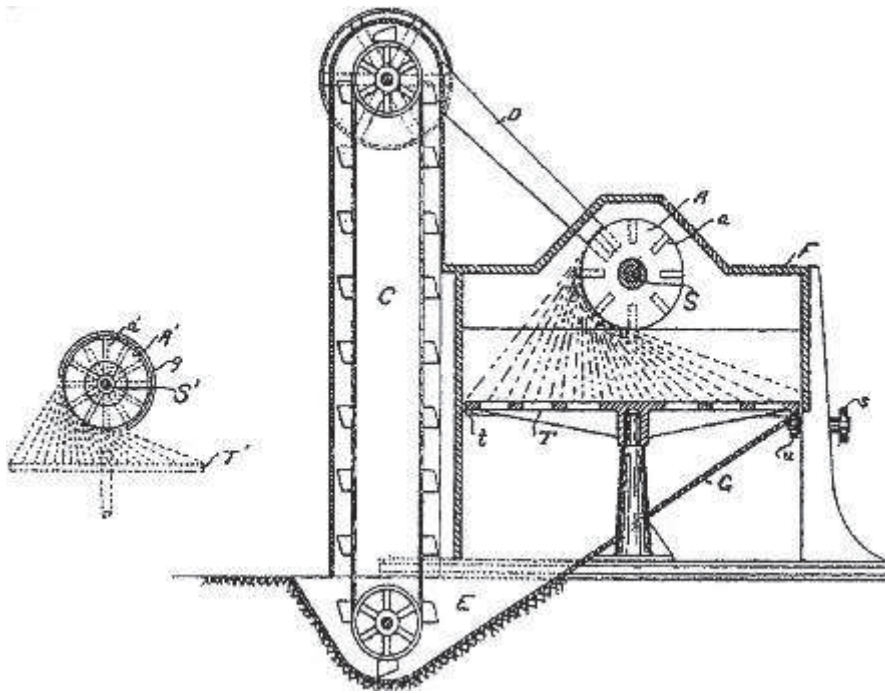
Pierwsze koło rzutowe śrutu opatentowane w 1870 roku przez Tilghmana [3]
